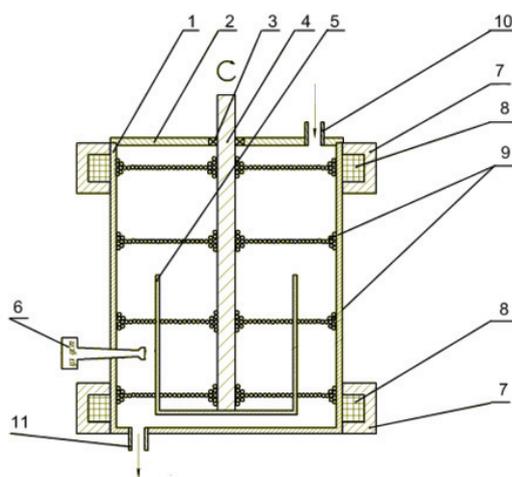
Конструктивная схема ЭММА – 2С (Патент РФ № 86493): 1 – цилиндрическая емкость; 2 – крышка; 3 – подшипник; 4 – ротор; 5 – лопасти; 6 – ультразвуковое устройство; 7 – ферромагнитное кольцо; 8 – ОУ; 9 – ферромагнитные элементы; 10 – загрузочный патрубок; 11 – разгрузочный патрубок
